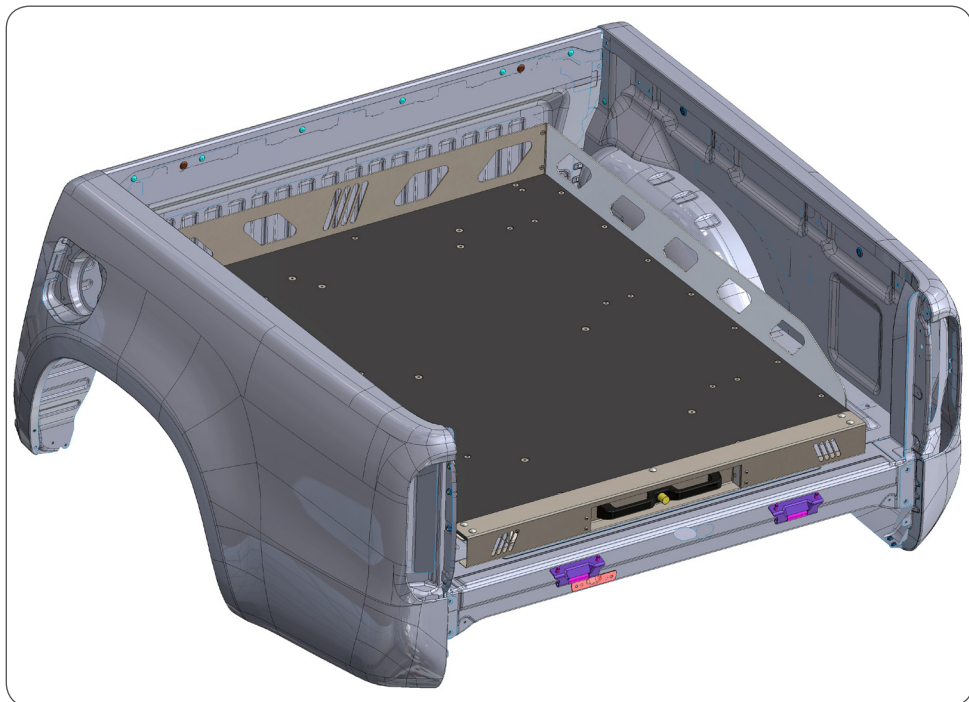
fertig eingebauter Schubladenauszug / fully assembled and mounted cargoslide
